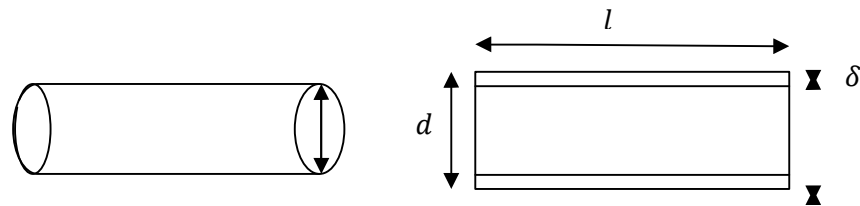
Pièce à chauffer sous forme d'un cylindre.
